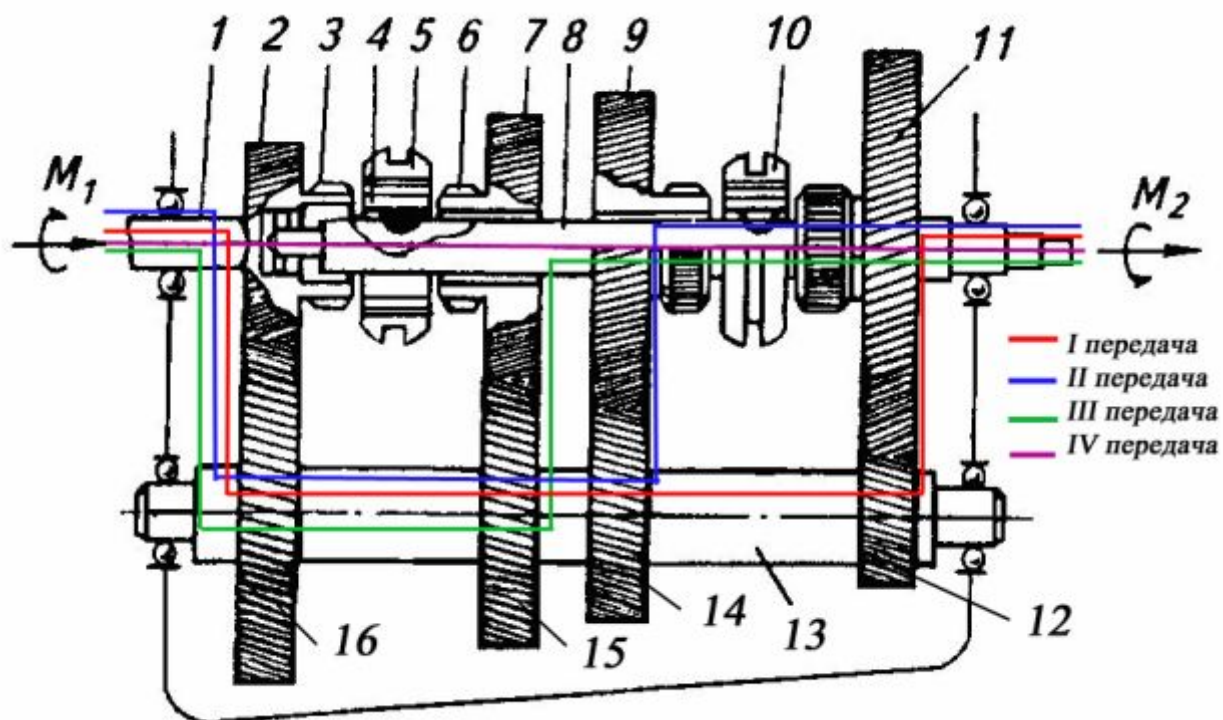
Схема трехвальной четырехступенчатой коробки передач автомобиля
